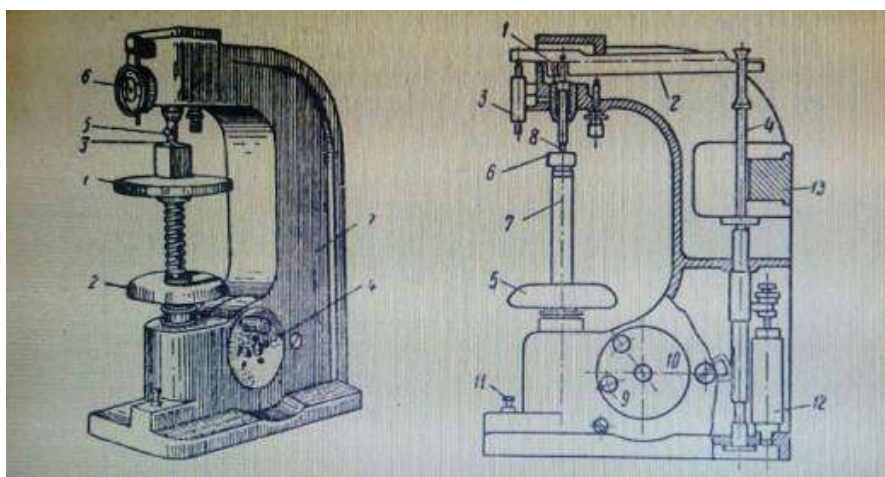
А-прибор Роквелла: 1-подставка, 2-маховик, 3-алмазный конус, 4-рукоятка, 5-наконечник, 6-индикатор, 7-станина; Б-схема дюрометра Роквелла
